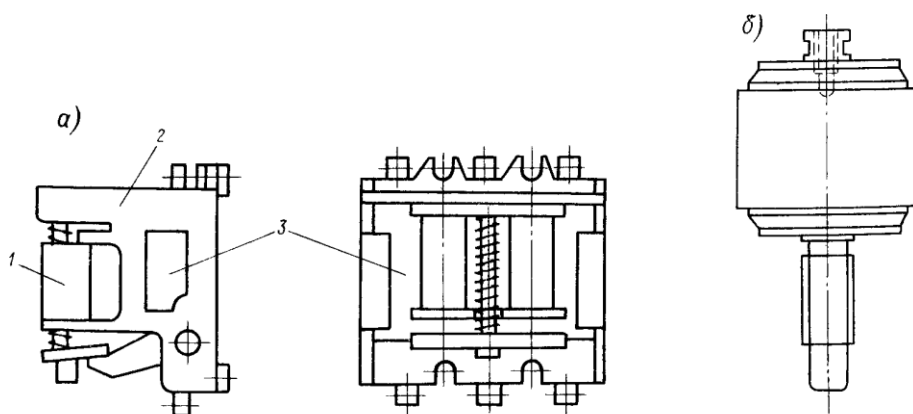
Вакуумний контактор: а - загальний вигляд, б - загальний вид вакуумної камери
